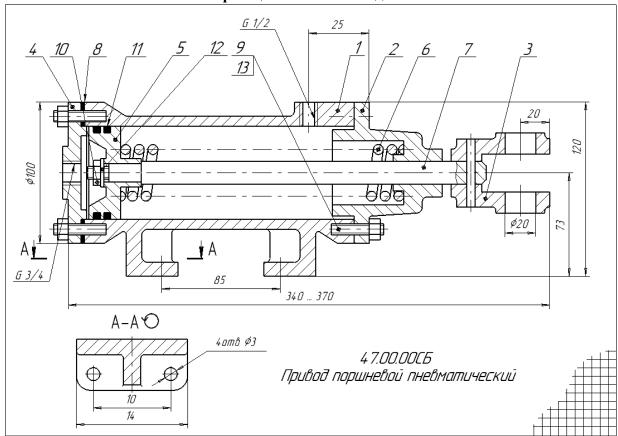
Образец выполнения задания ИГ 9.3 Сборочный чертеж
